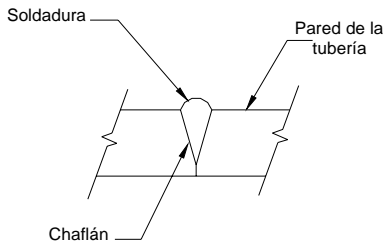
Construcción Típica de Uniones de Soldadura de Extrusión
